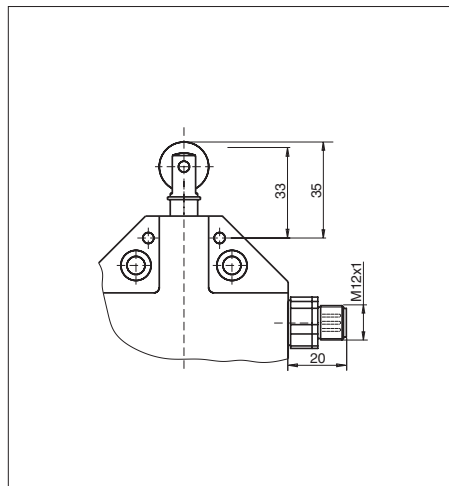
Maßzeichnung N1A... mit Steckverbinder M12
